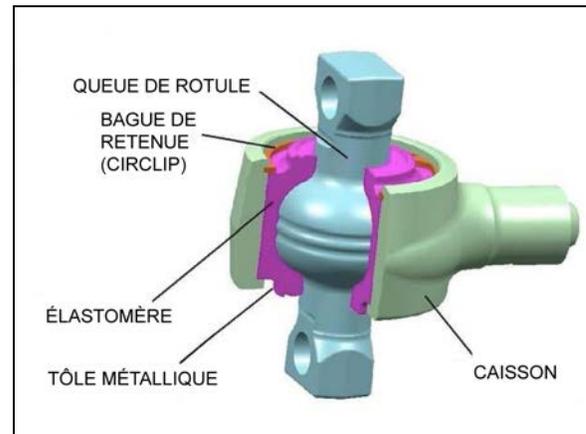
CONSTRUCTION DU JOINT SPHÉRIQUE 16186
